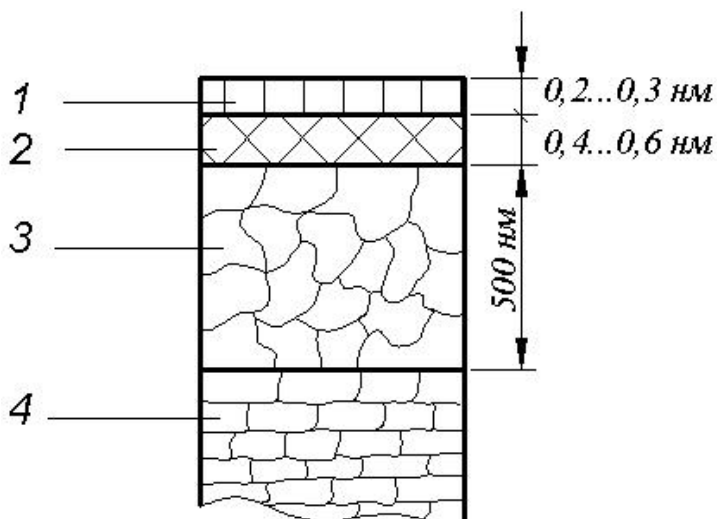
Структура поверхневого шару шліфованої деталі з вуглецевої сталі
